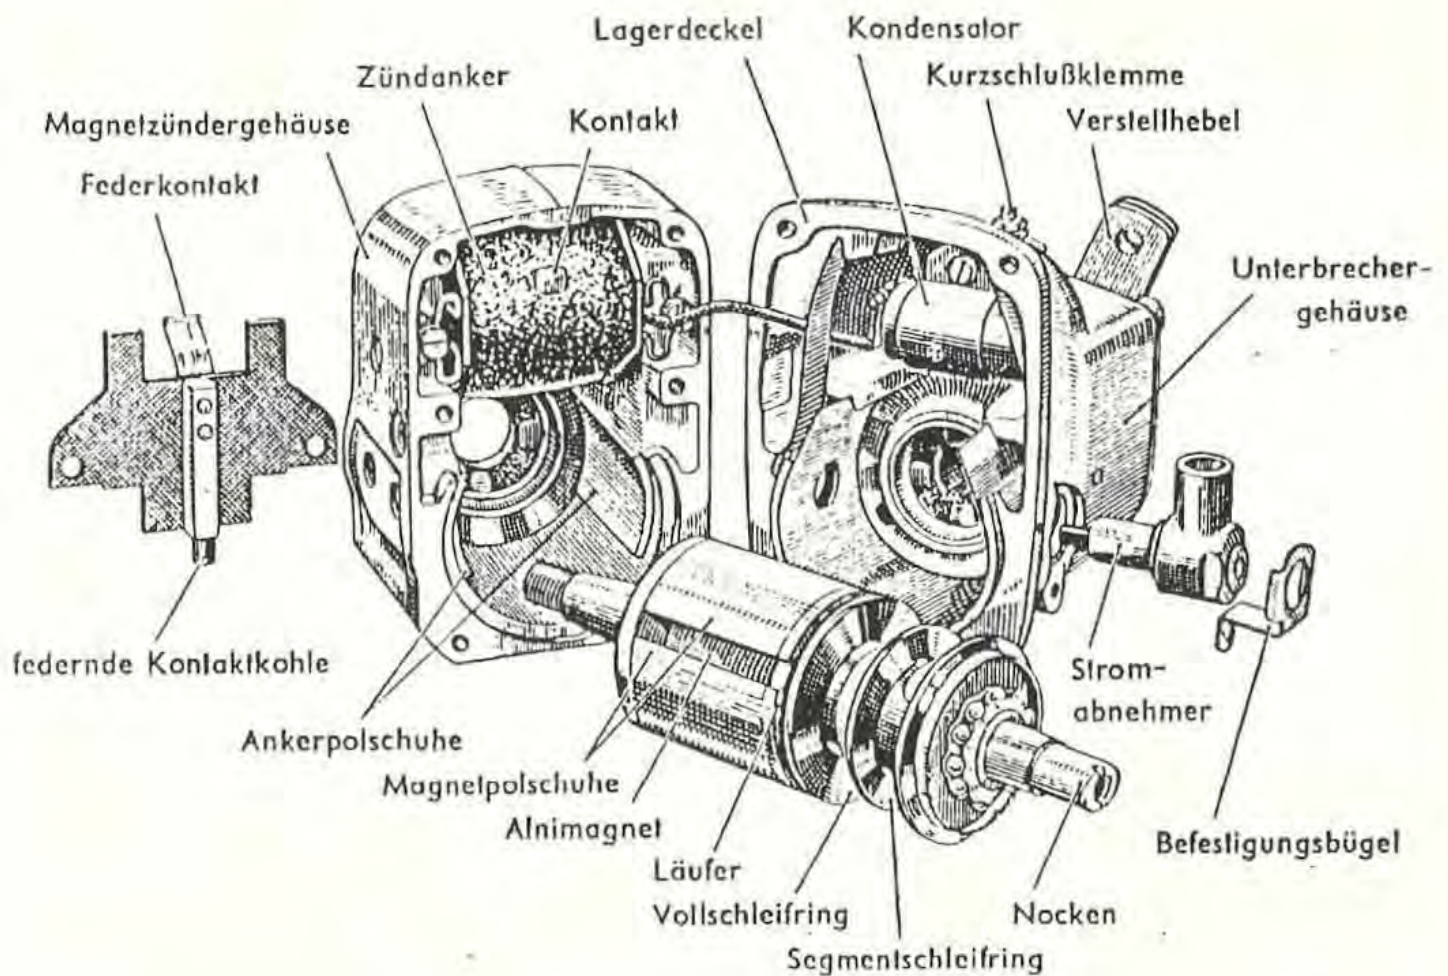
Bosch-Magnetzündler Type MZ/JF 2 für Zweizylindermotor – Innenansicht
